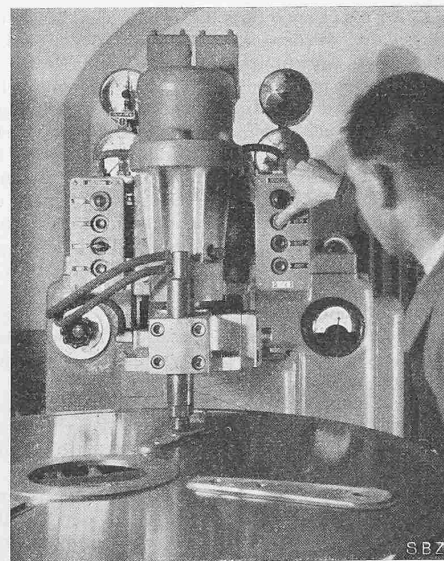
Stirnseite des Schweissarmes einer Maschine für 10 verschiedene Schweissprogramme
